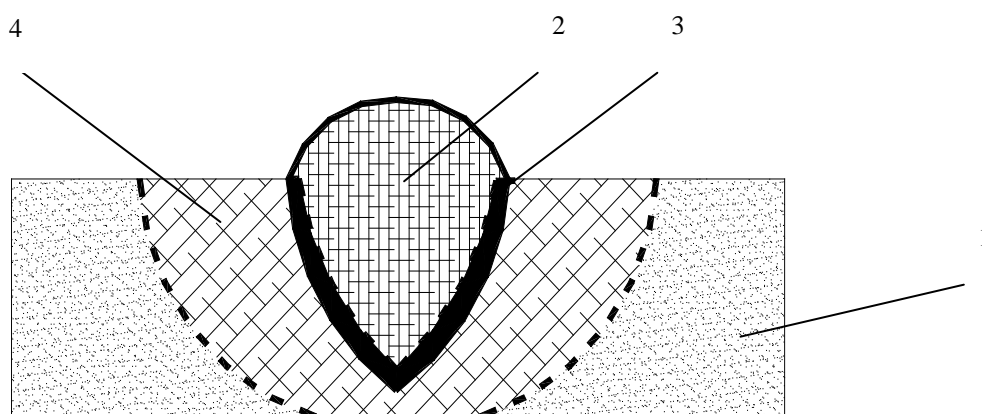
Строение сварочного шва. 1 – основной металл; 2 – сварной шов (наплавленный металл); 3 – зона сплавления; 4 – зона термического влияния
